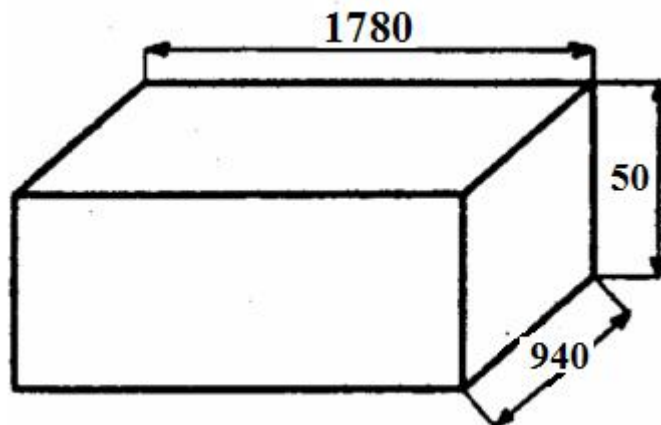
Forme et dimensions de l'ébauche après correction
